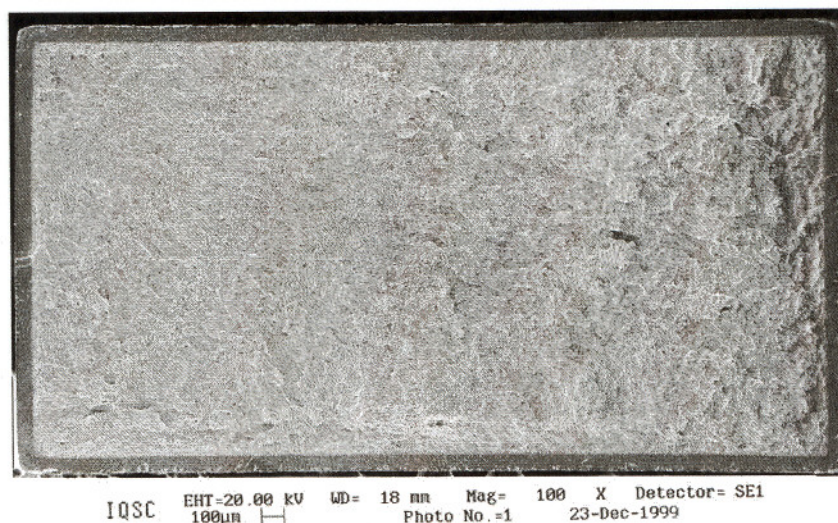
Superfície de fratura de tração de um corpo de prova nitretado.
